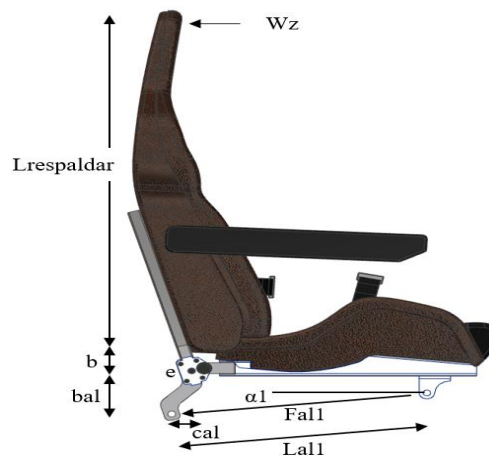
DCL Asiento/Respaldar - posición inicial
